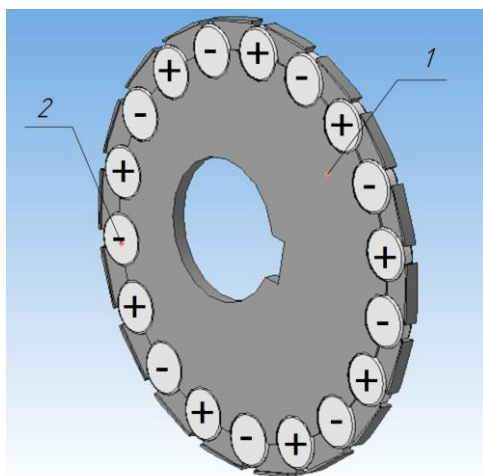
Дисковий інструмент для оброблення МАО
